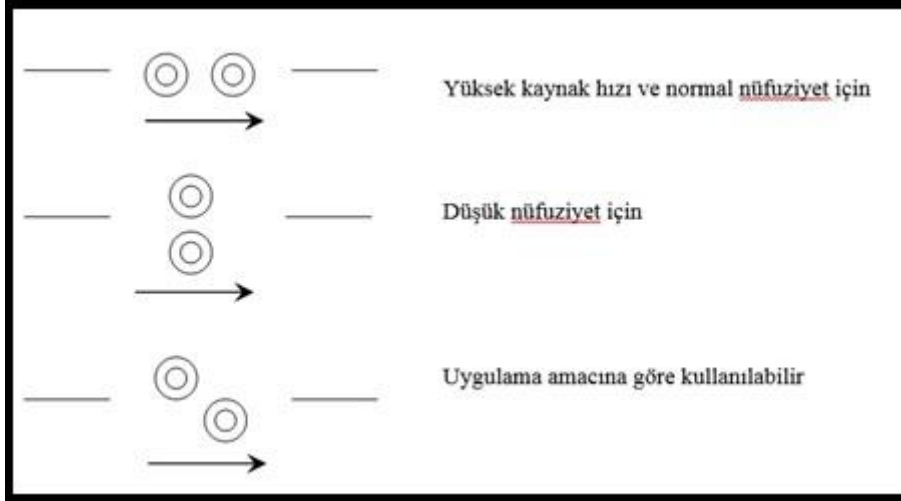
Bir tandem tozaltı düzeneğinin şeması
